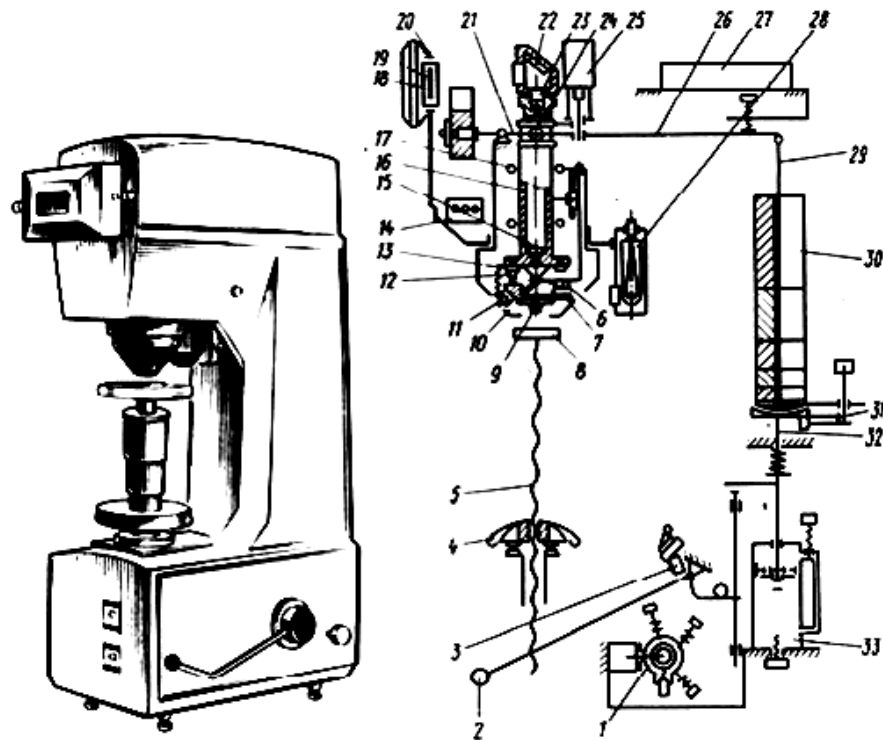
Прилад для вимірювання твердості ТП-7Р-1
